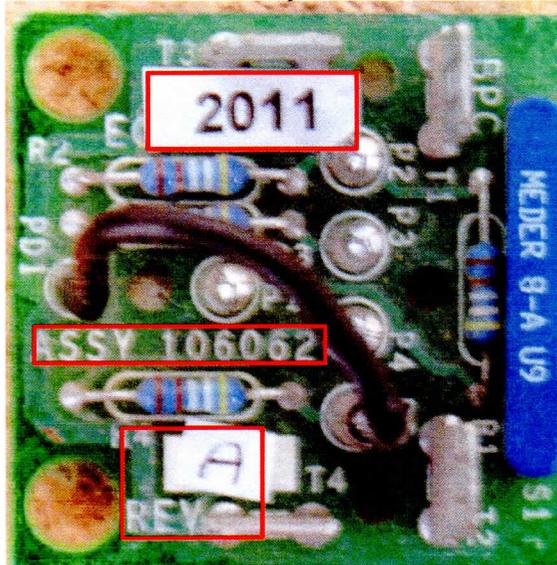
Tarjeta HANDLE SWICHT identificada con número de parte 106062, vista cara de soldadura. Ver detalle en cuadro rojo.
